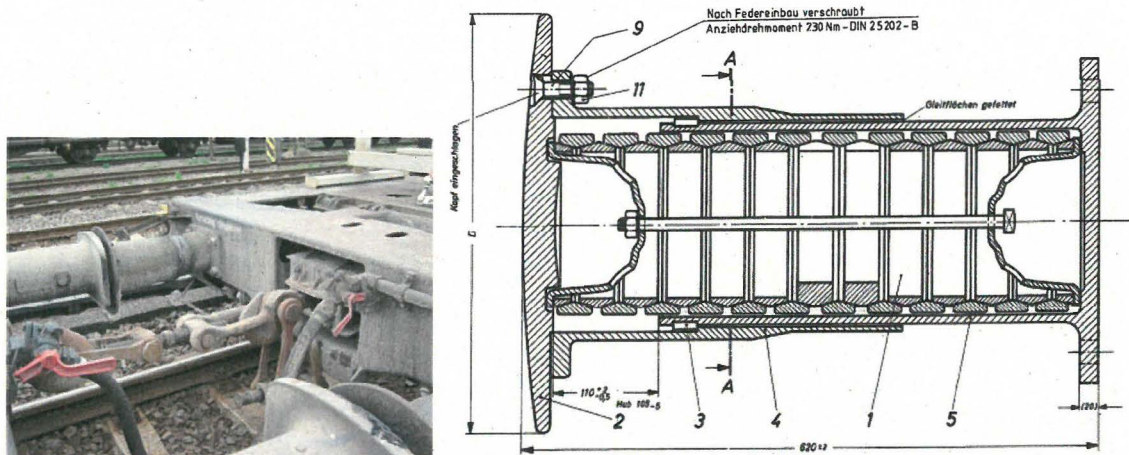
Bild Puffer und Zughaken des Unfallzuges und Pufferzeichnung aus Zeichnung Fwg 000.06.003.20 Hülspuffer drehbar 105mm Hub 620mm Länge 59Mp Endkraft
